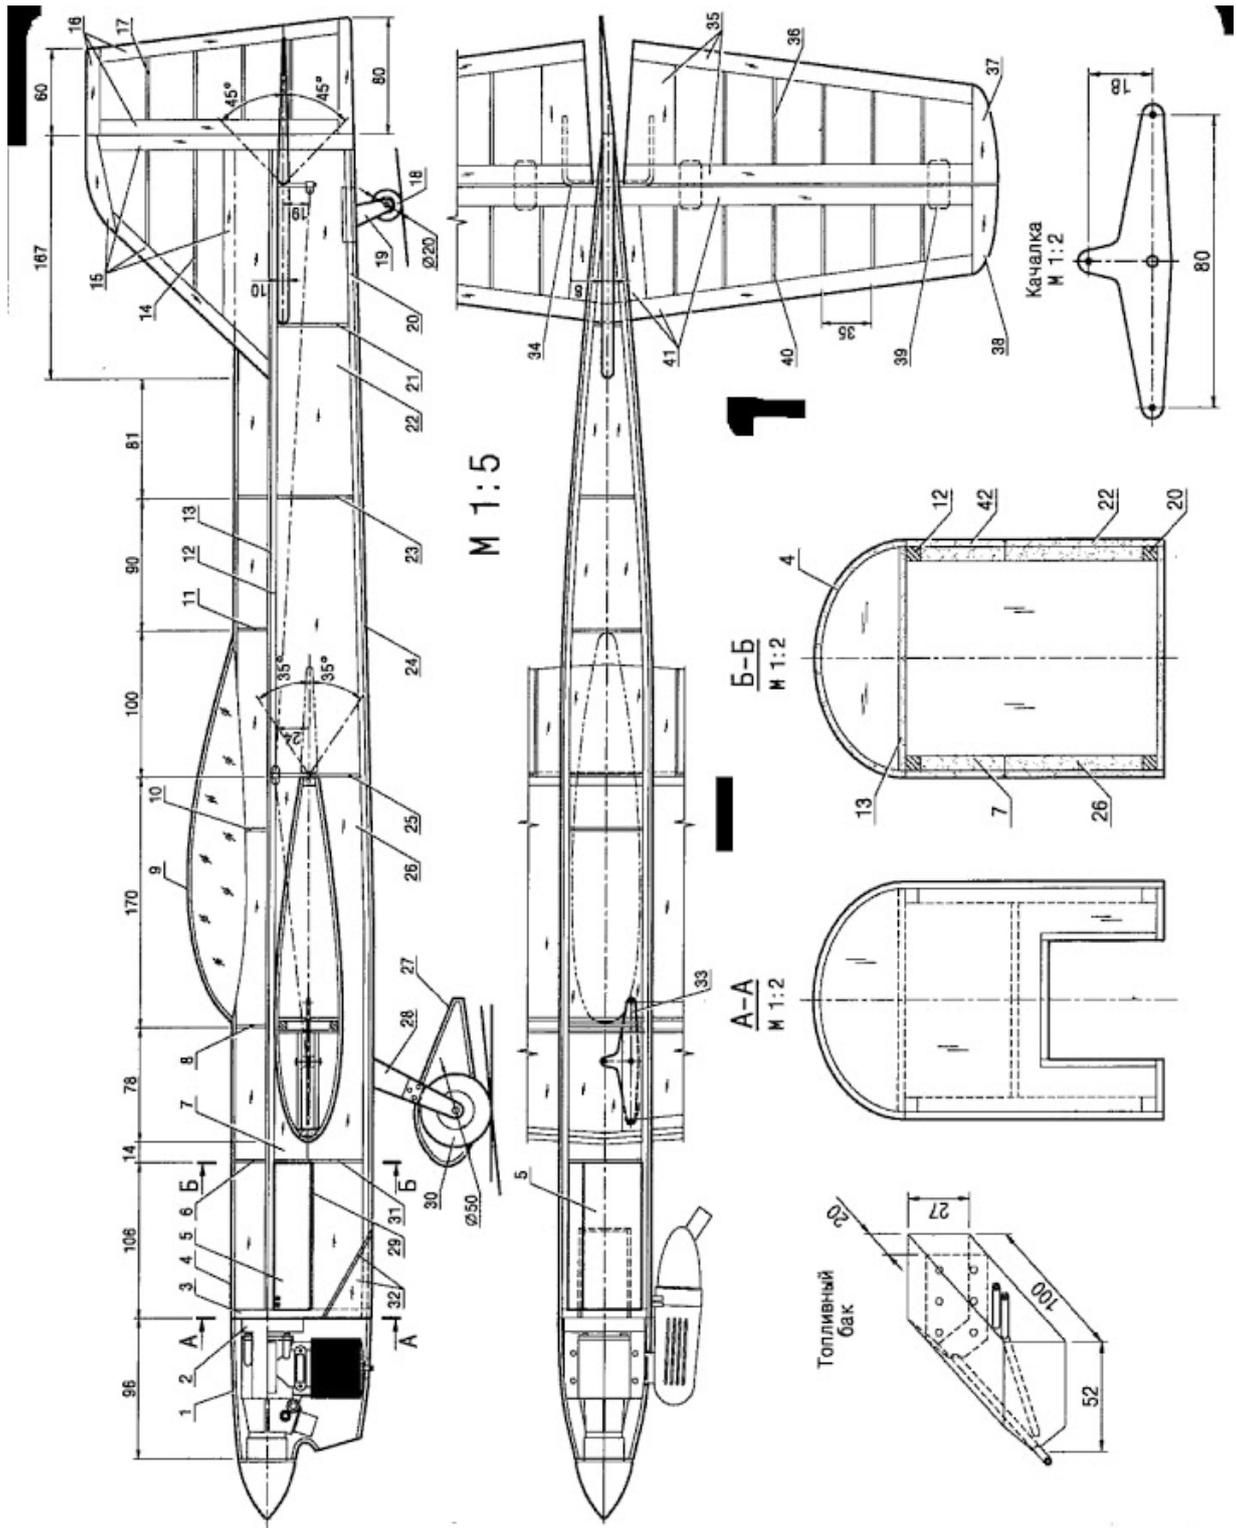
Чертёж кордовой модели F-2-B. Вид сверху и сбоку
